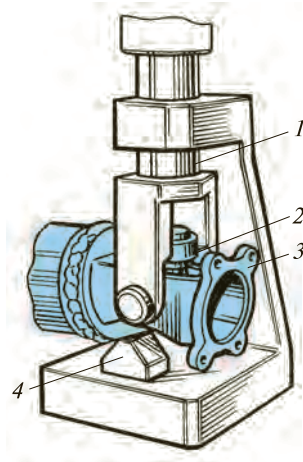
Приспособление для выпрессовки корпуса игольчатого подшипника карданного вала автомобиля «Москвич-2140»: 1 — скоба; 2 — проушина вилки; 3 — карданный вал; 4 — упор
